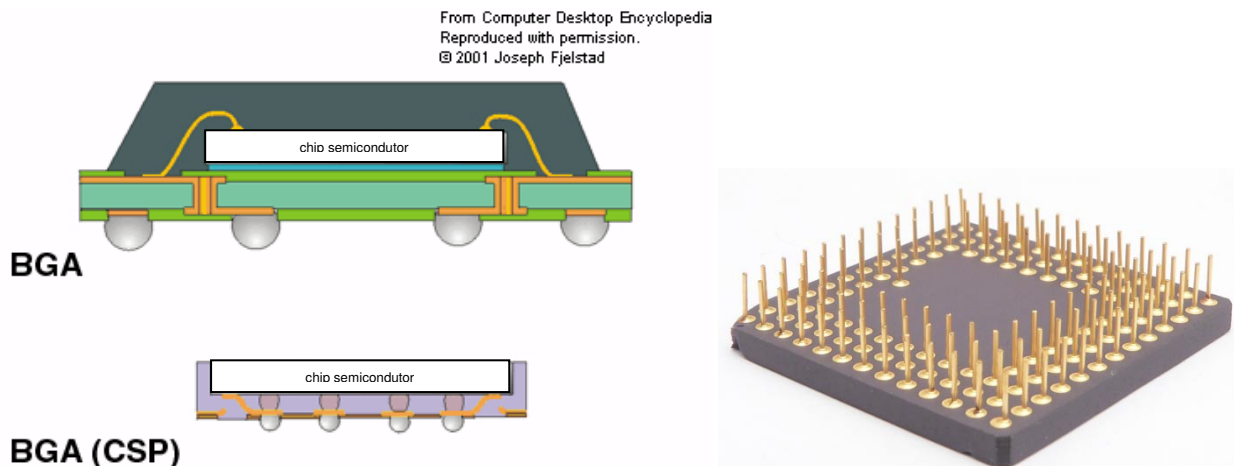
Exemplos de empacotamento BGA (solda do chip seguida de microsolda do fio e montagem *flip-chip*) e um empacotamento CGA (à direita). [15]
